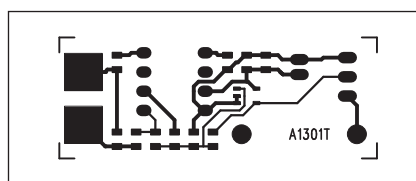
Obrazec desky spojů displeje (strana BOTTOM)
